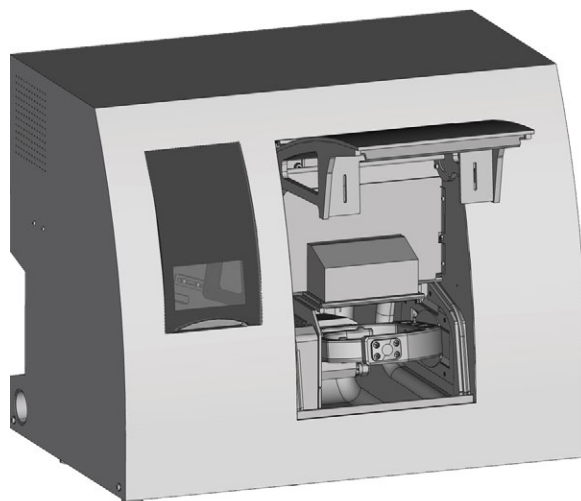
PORTE DE LA CHAMBRE DE TRAVAIL
